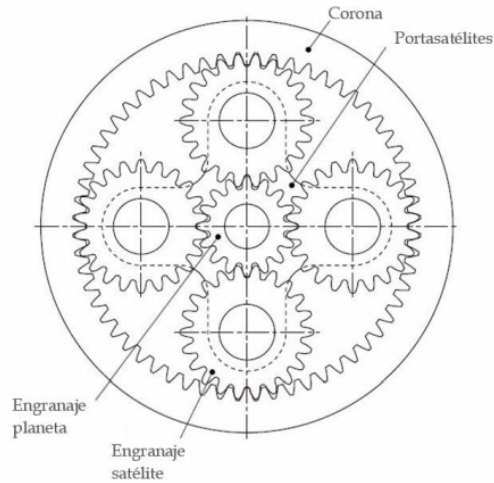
Partes del mecanismo básico de engranajes planetarios.
